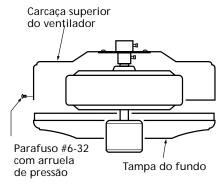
Fixando a tampa do fundo à carcaça superior do ventilador
